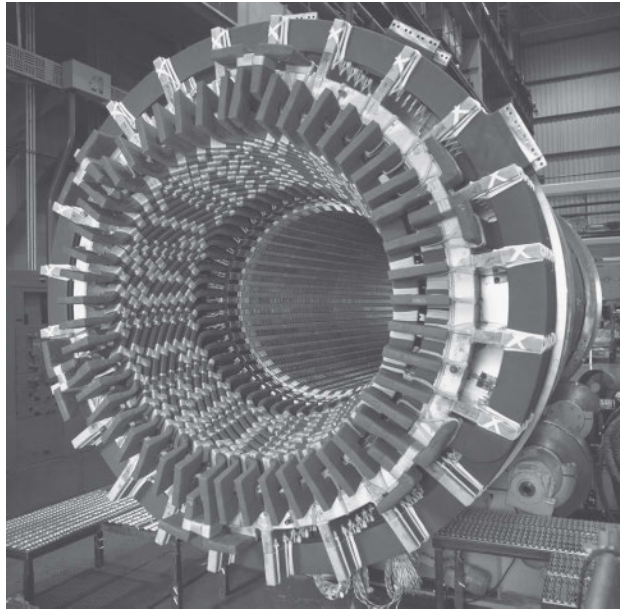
Vista da extremidade do estator de um gerador a turbina de 16,5 kV, 275 MVA e 3600 rpm. (Foto cortesia da empresa Siemens.)
